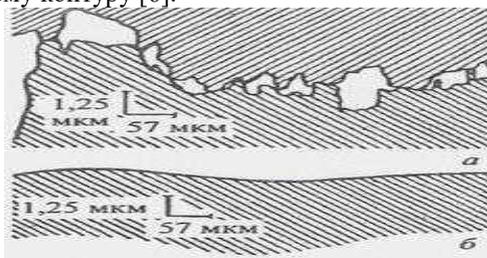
Профиль поверхности: а - двух собранных медных деталей перед ультразвуковой сваркой; б - нижней детали после воздействия ультразвука [10].
